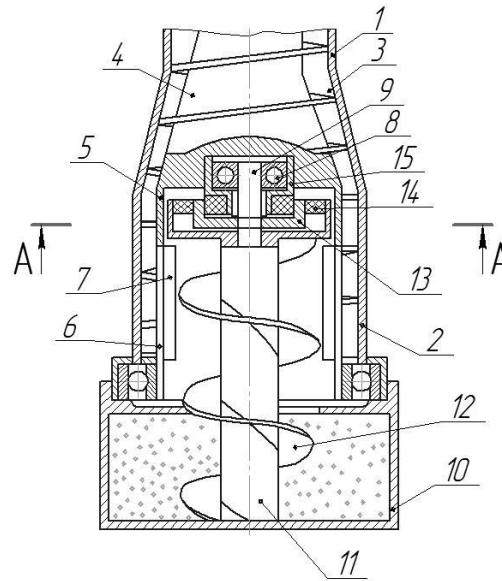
Забірний пристрій гвинтового конвеєра
